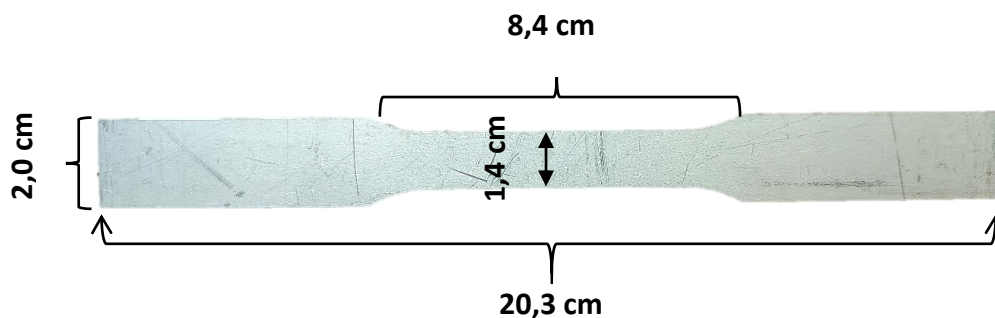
Dimensiones de la probeta AISI 304L. Espesor de 5 mm.
